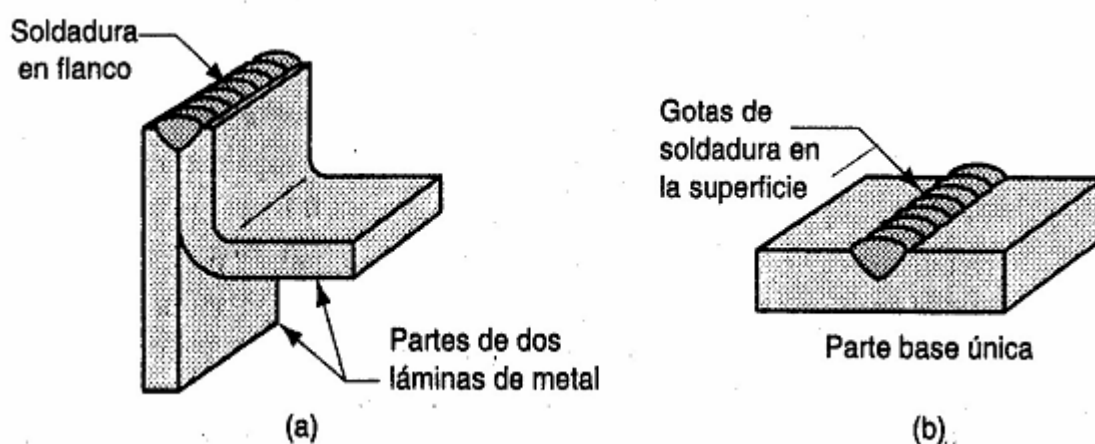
(a) Soldadura en flanco y (b) Soldadura en superficie
